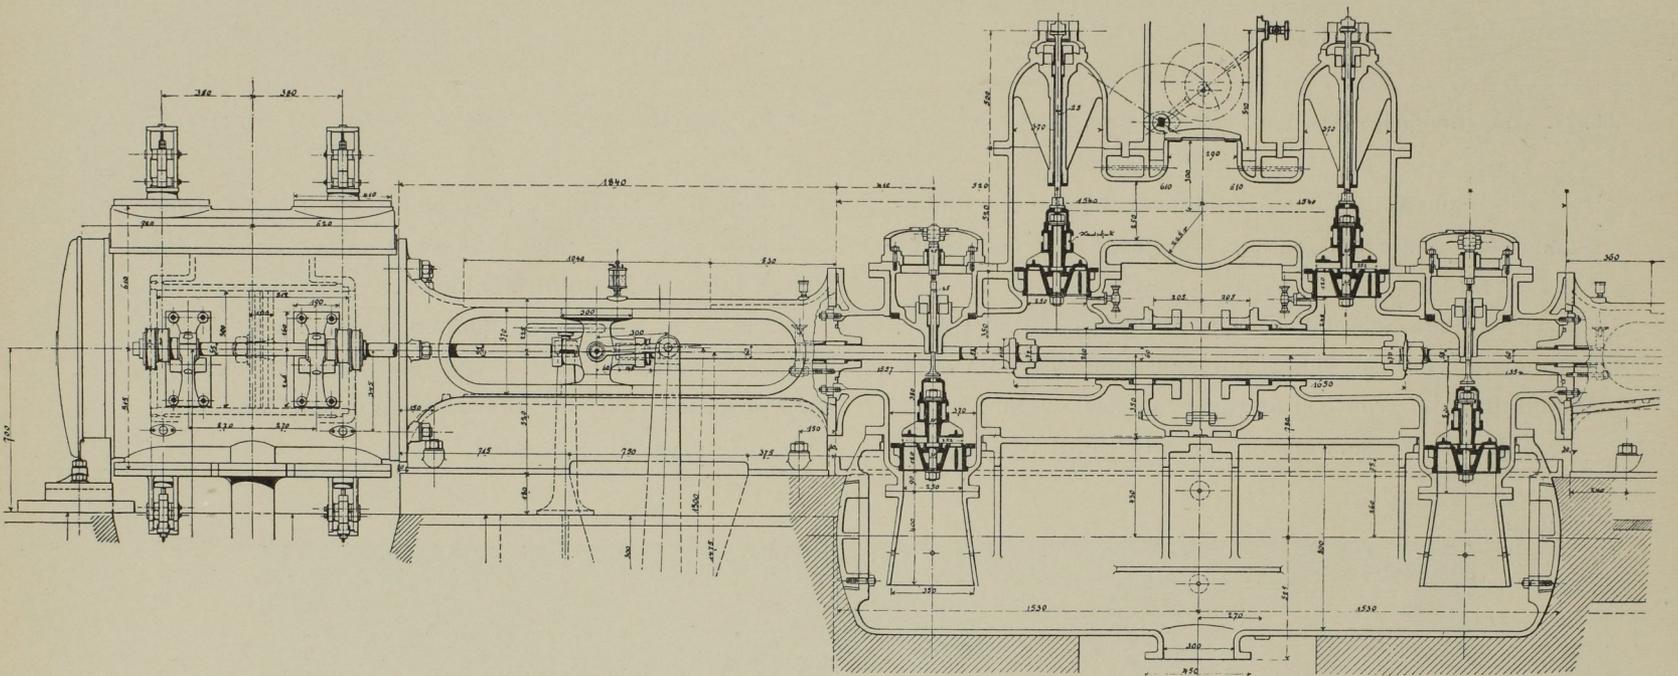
Längsschnitt der Druckpumpe. Massst. 1:30.
